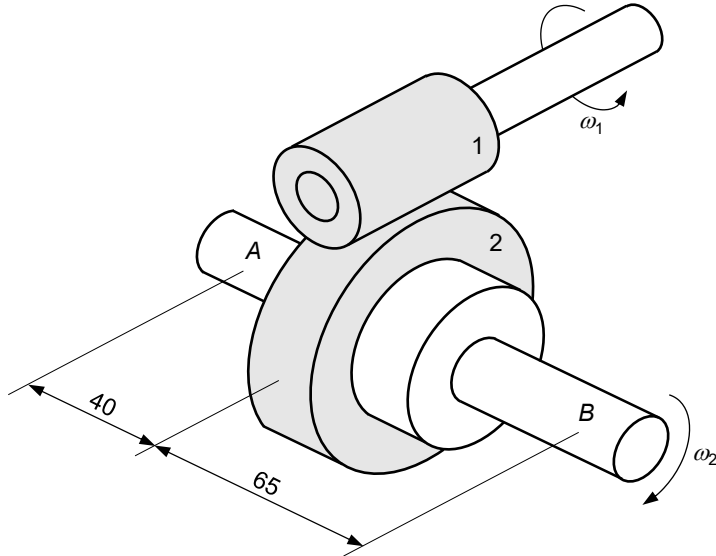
Engrenagem de parafuso sem-fim roda helicoidal.
